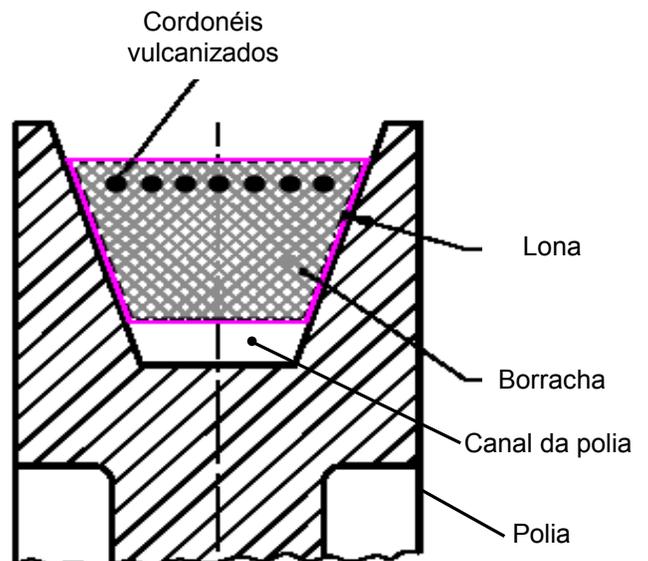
Vista em corte da seção transversal de uma correia trapezoidal
